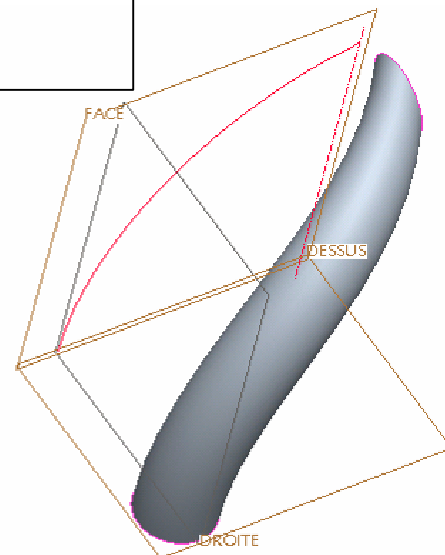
Contrôle du plan de section normal à la trajectoire.
